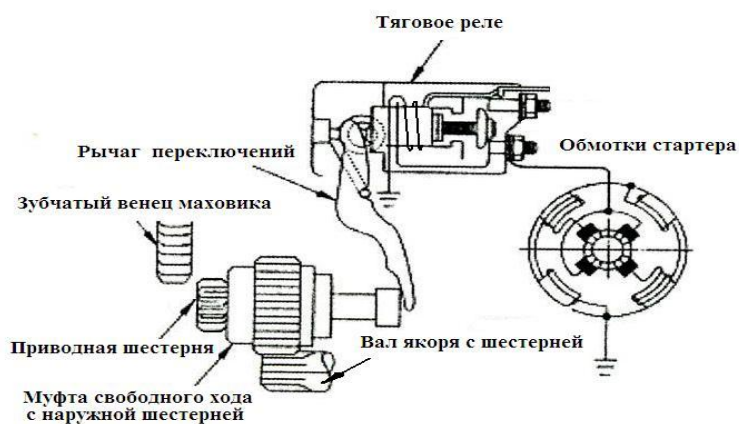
Механизм привода стартера S25-168 автобусов ISUZU
